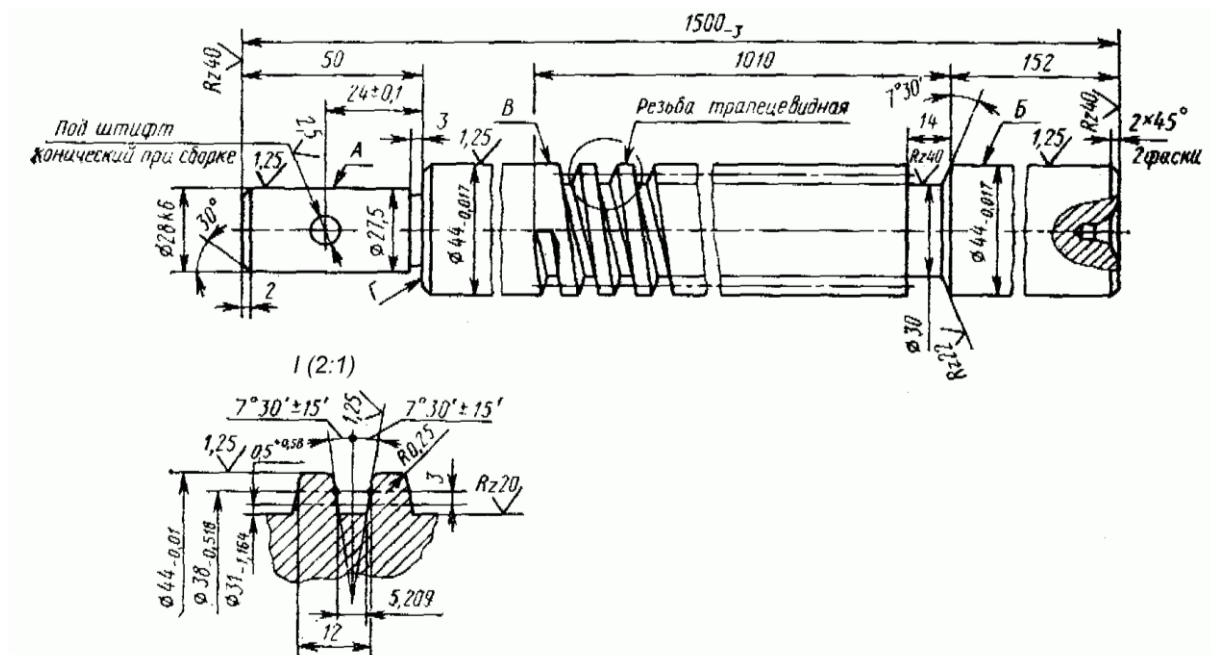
Ходовий гвинт токарного верстата 16К20
